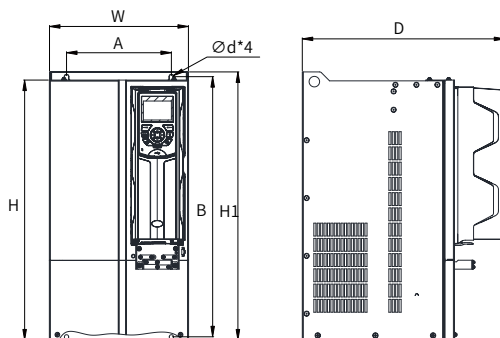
Габаритные и монтажные размеры конструкций Т2 - Т9
